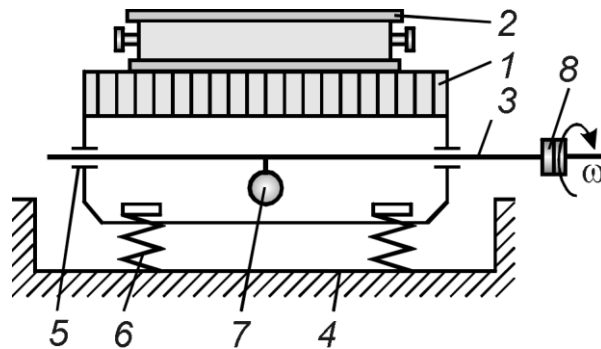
Схема вибивної інерційної решітки: 1 – корпус решітки. 2 – опока. 3 – приводний вал. 4 – рама. 5 – опори вала. 6 – пружинна підвіска. 7 – грузи. 8 – муфта.
